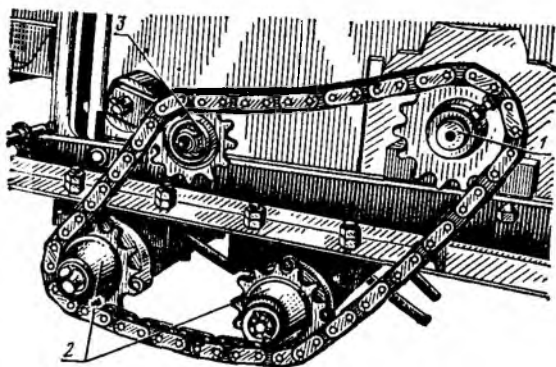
Привод роторного приспособления картофелекопателя КТН-2Б:
